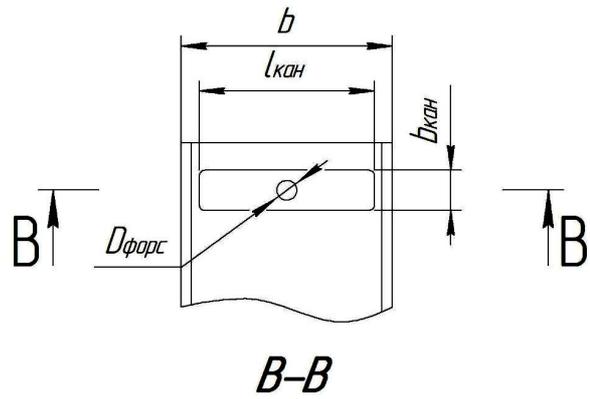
Геометрия подвода смазки в рабочую зону опорного подшипника
